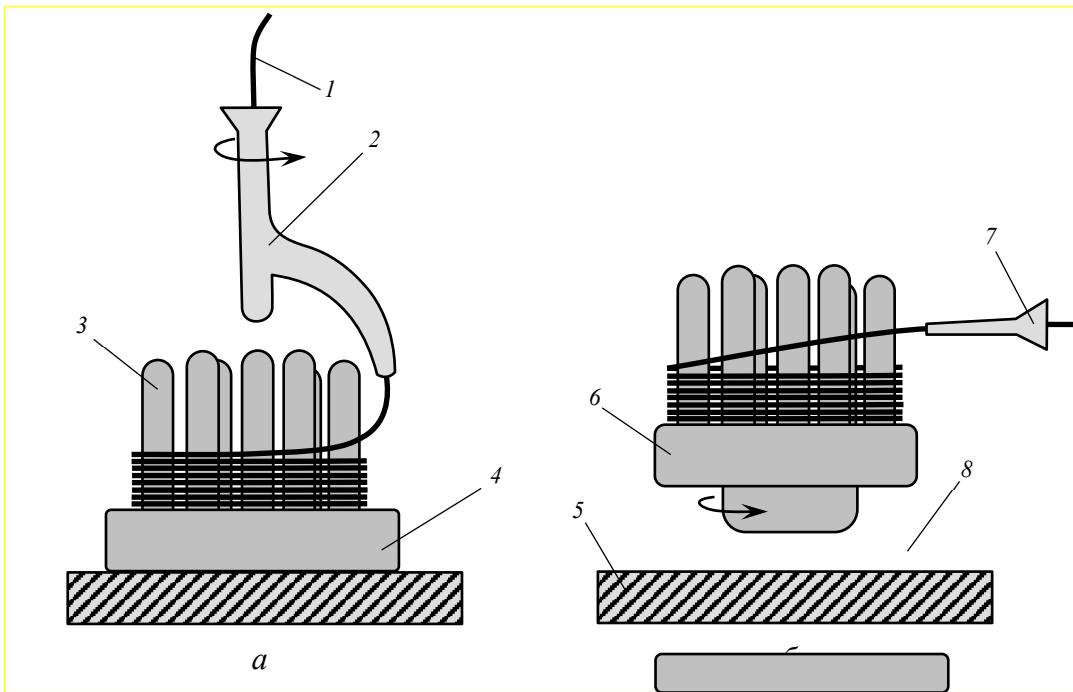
Дрібносортні моталки з бунтом: а - стаціонарним; б - обертовим (1 - Катанка; 2 , 7 - трубки; 3 - палець; 4 , 8 - Нерухомі плити; 5 - фундамент; 6 - Грибоподібний шпиндель)
